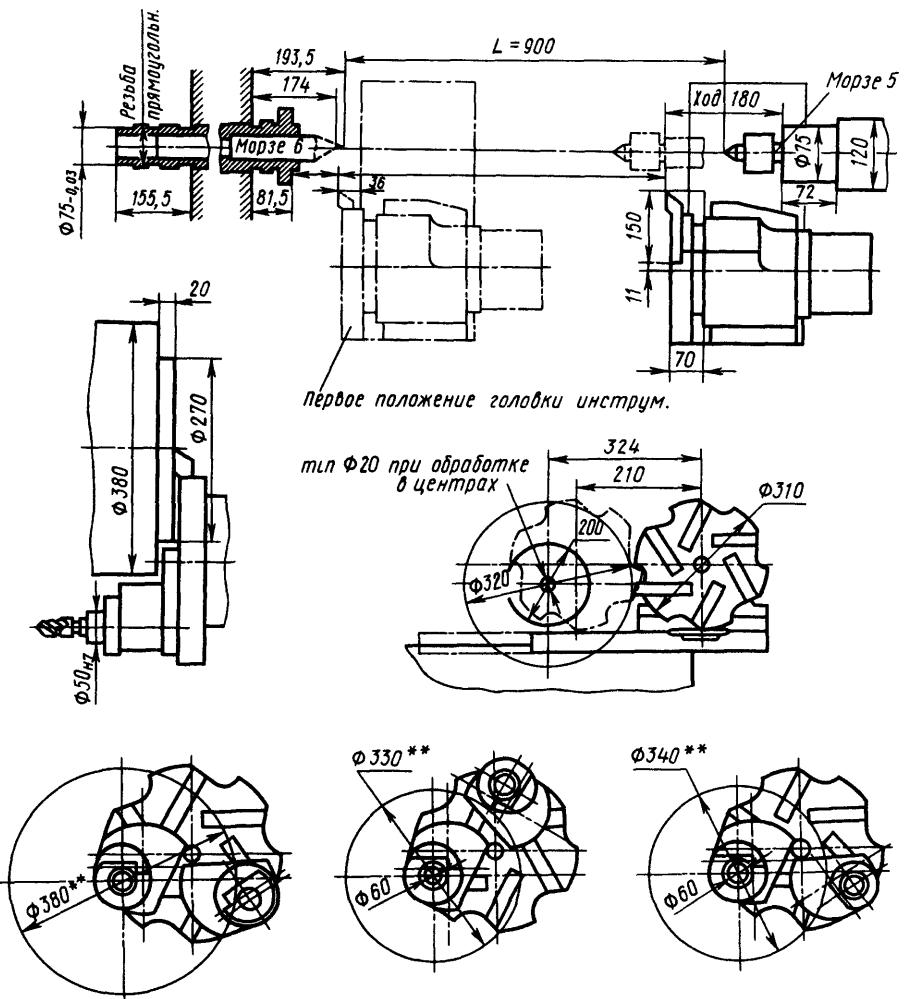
Схема технологических возможностей станков 16А20Ф3С39 и 16А20Ф3С32 с шестипозиционной автоматической головкой
